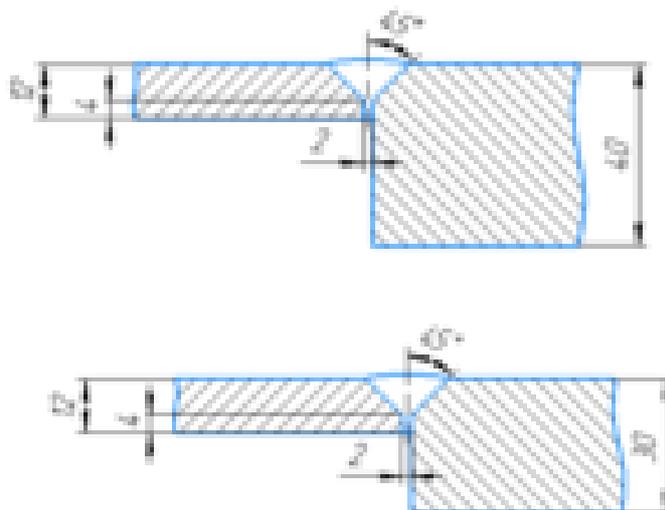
Общий вид сварных швов №1 и №2
